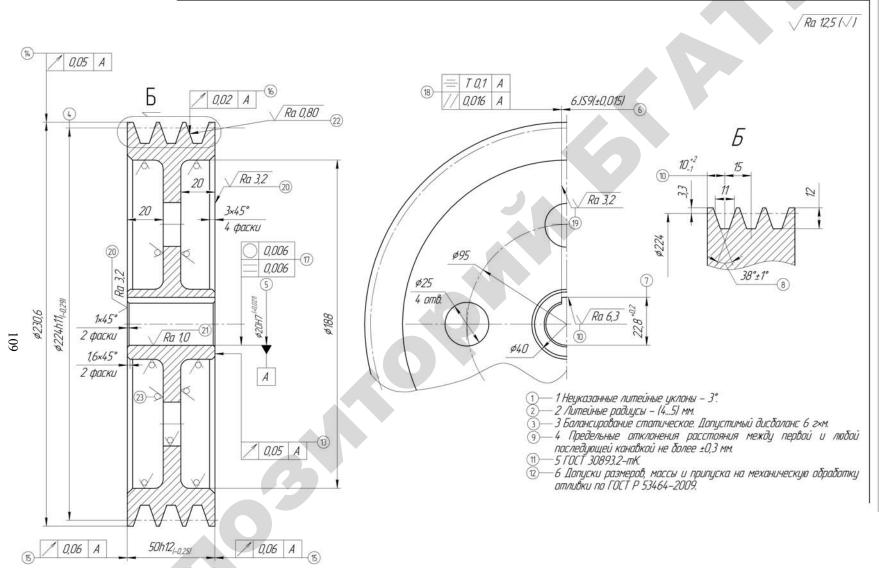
Схема простановки размеров и показателей точности для шкива клиноременной передачи
